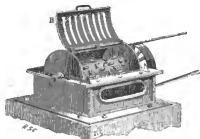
Loup ou diable pour le pétrissage du caoutchouc.
